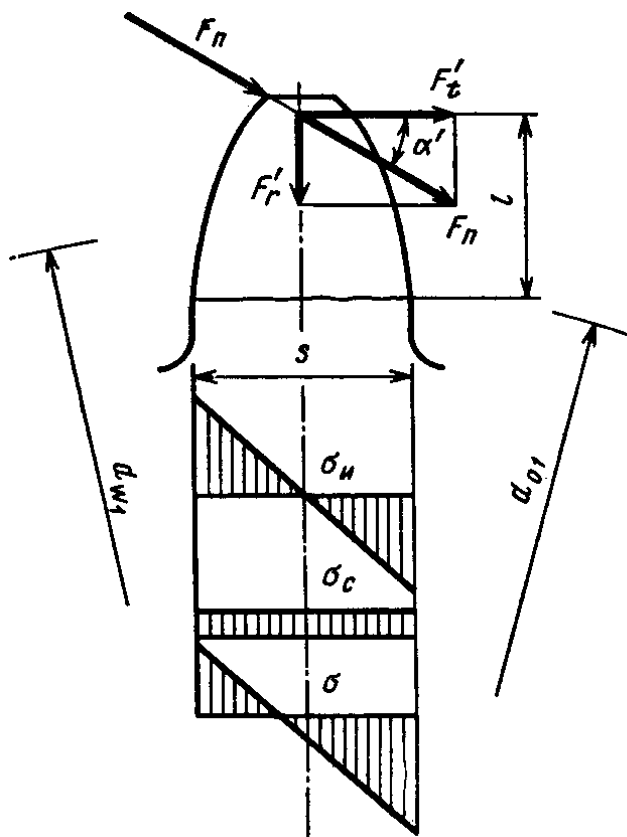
Розрахункова схема навантаження зубця циліндричного зубчастого колеса
